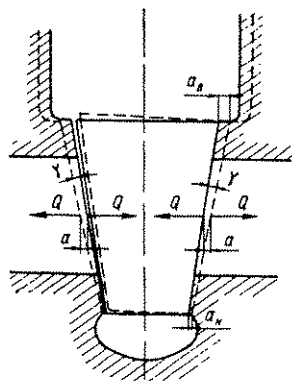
Перемещения уплотняющих поверхностей корпуса и клина при деформации задвижки
